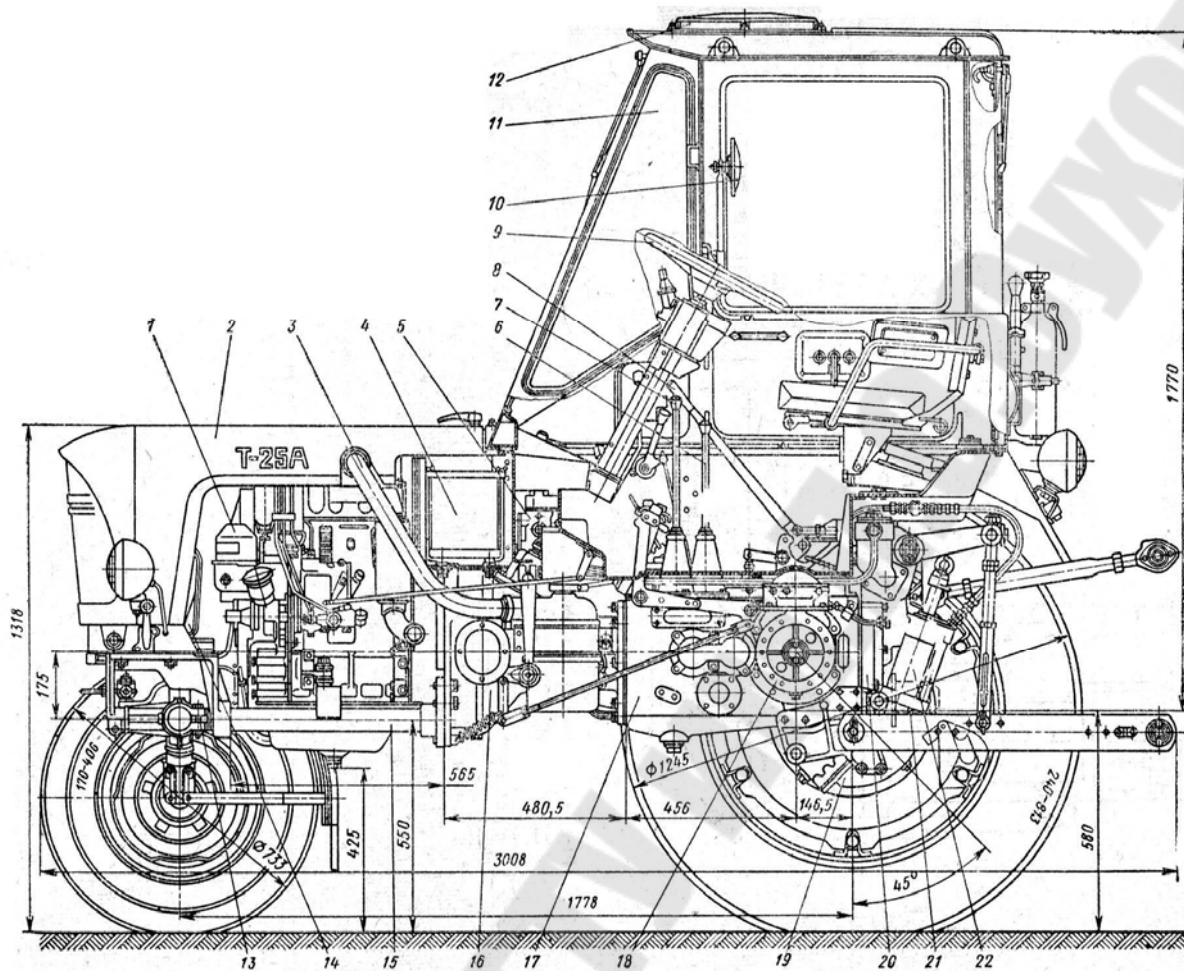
Размерная схема реверсивного трактора Т-25А:
